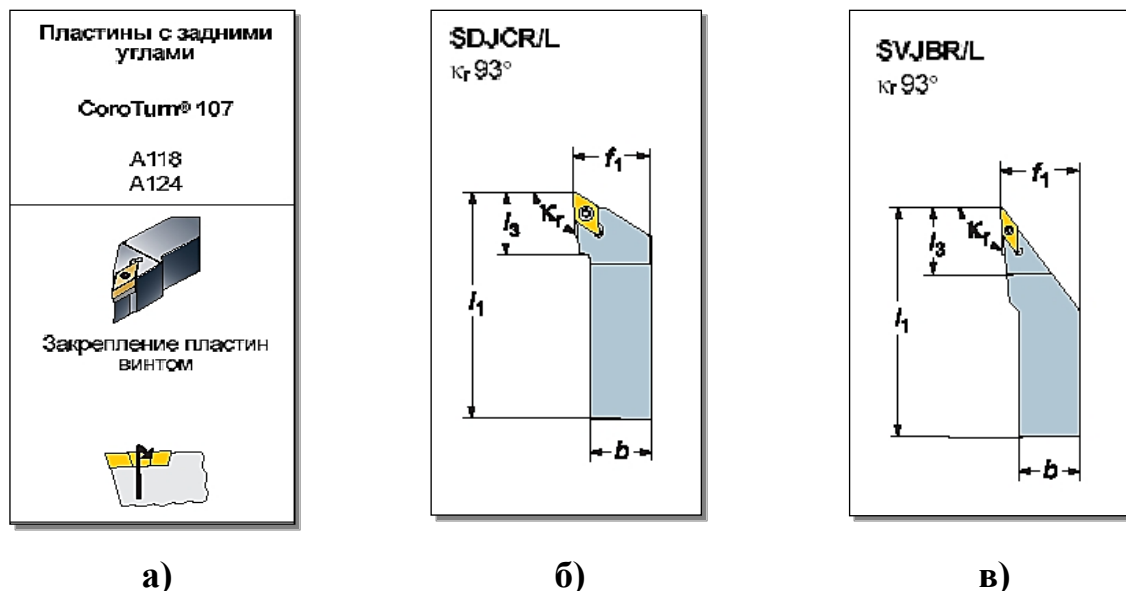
Вид вибраного інструменту: а)вибраний тип; б) для точіння циліндричних поверхонь; в)для точіння фасок;
